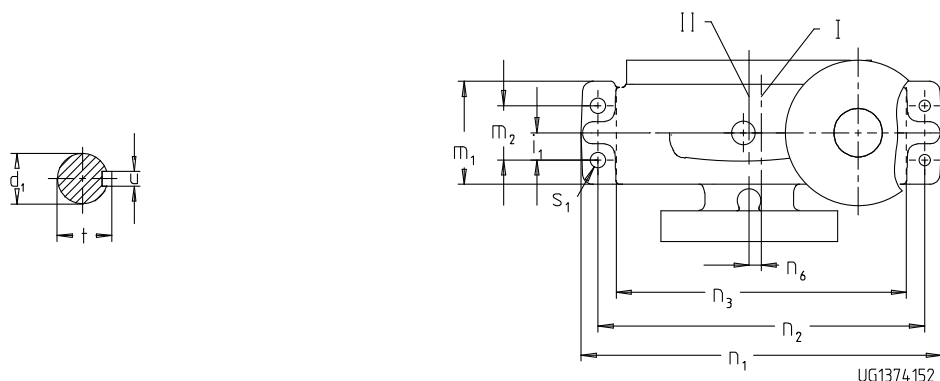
Размеры крепления по лапам и конца вала, стандартные типоразмеры
